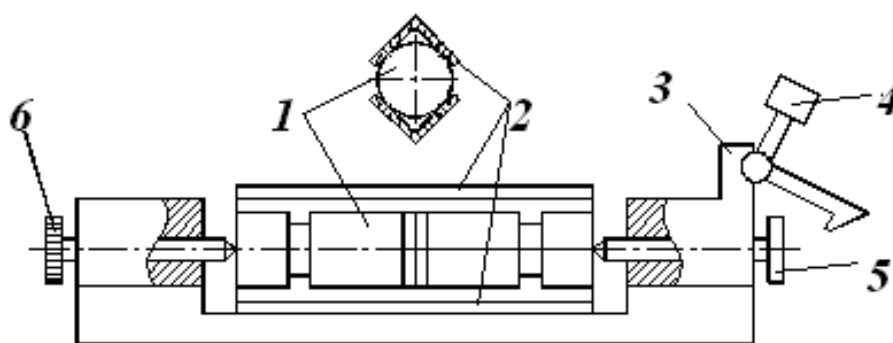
Схема приспособления для формирования адгезионного соединения
